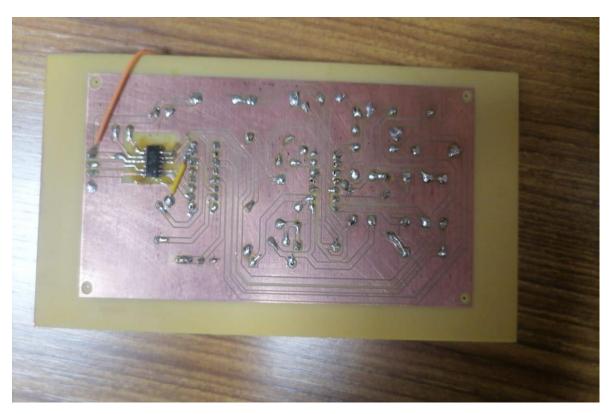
Sonar Sistem Tasarımı HC RS04 PCB Tasarımı
